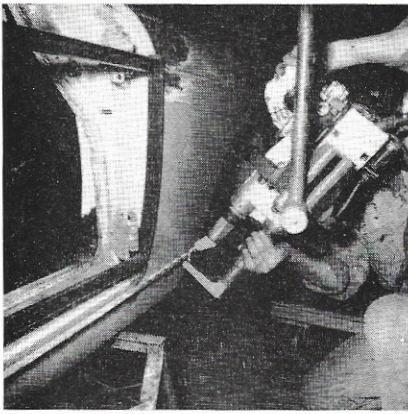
Soudage de l'aile avant sur tôle de bas de marche. Pince ARO.
